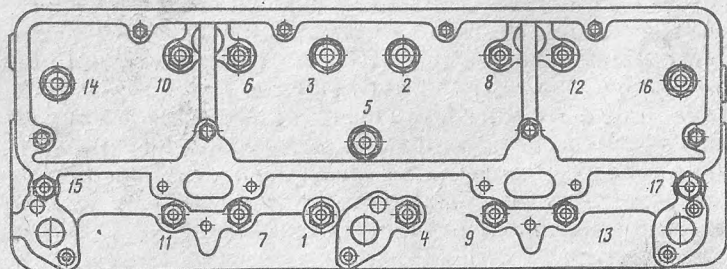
Последовательность затяжки гаек крепления головки цилиндров.
